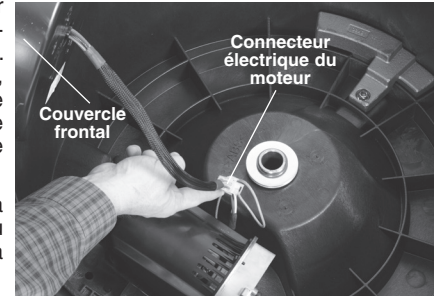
Ouverture du couvercle frontal du dégorgeoir
